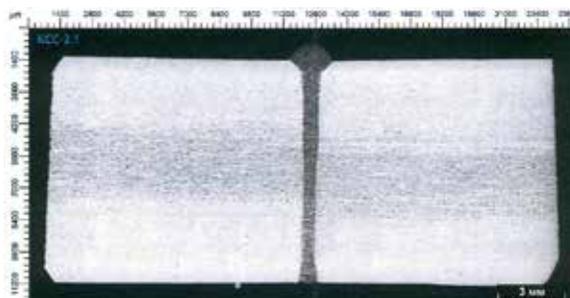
Поперечный макрошлиф сварного соединения образцов толщиной 10 мм
